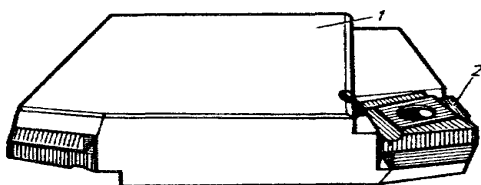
Мірна розточувальна пластинка з механічним кріпленням чотирилезових твердосплавних пластинок: 1 - корпус; 2 - непереточувана твердосплавна пластинка
